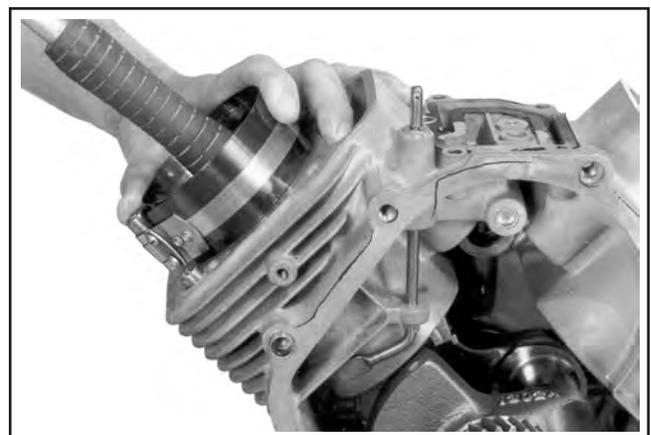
Installation der Pleuelstange unter Verwendung eines Pleuelstangenkompressorwerkzeugs.
